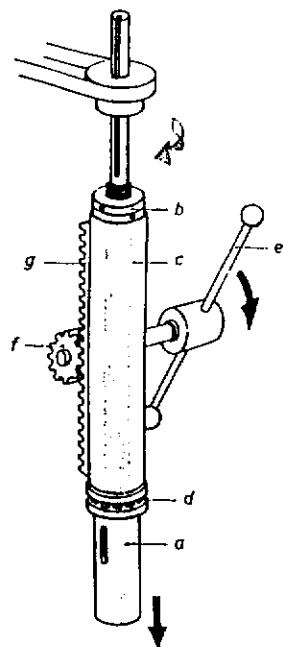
Guía del husillo de taladrar: a) Husillo; b) tuercas de anillo; c) casquillo; d) rodamientos de bolas; e) palanca; f) rueda dentada; g) cremallera.
